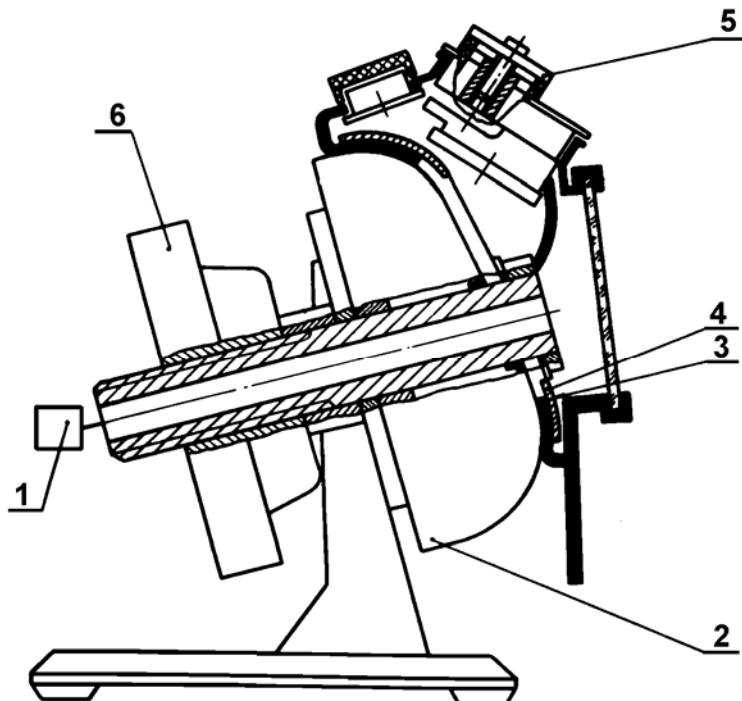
Схема проверки маски на герметичности с приспособлением ПМ-3
